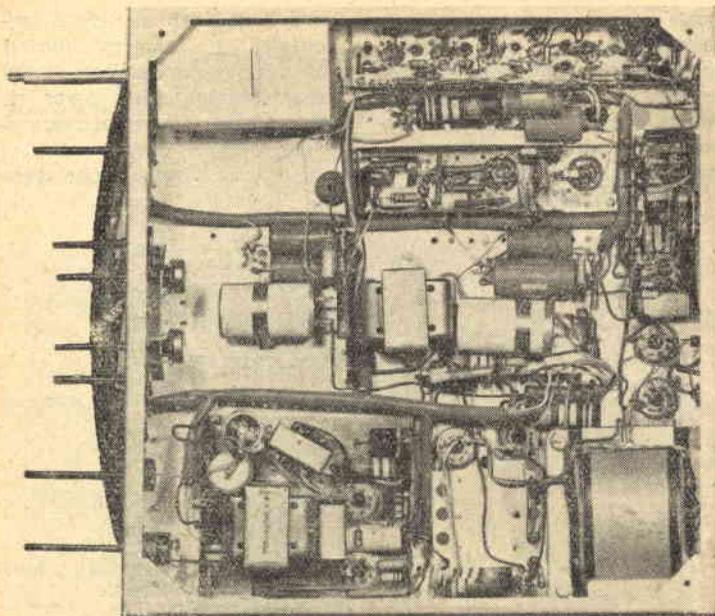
Vista dall'alto del televisore a cablaggio ultimato.
